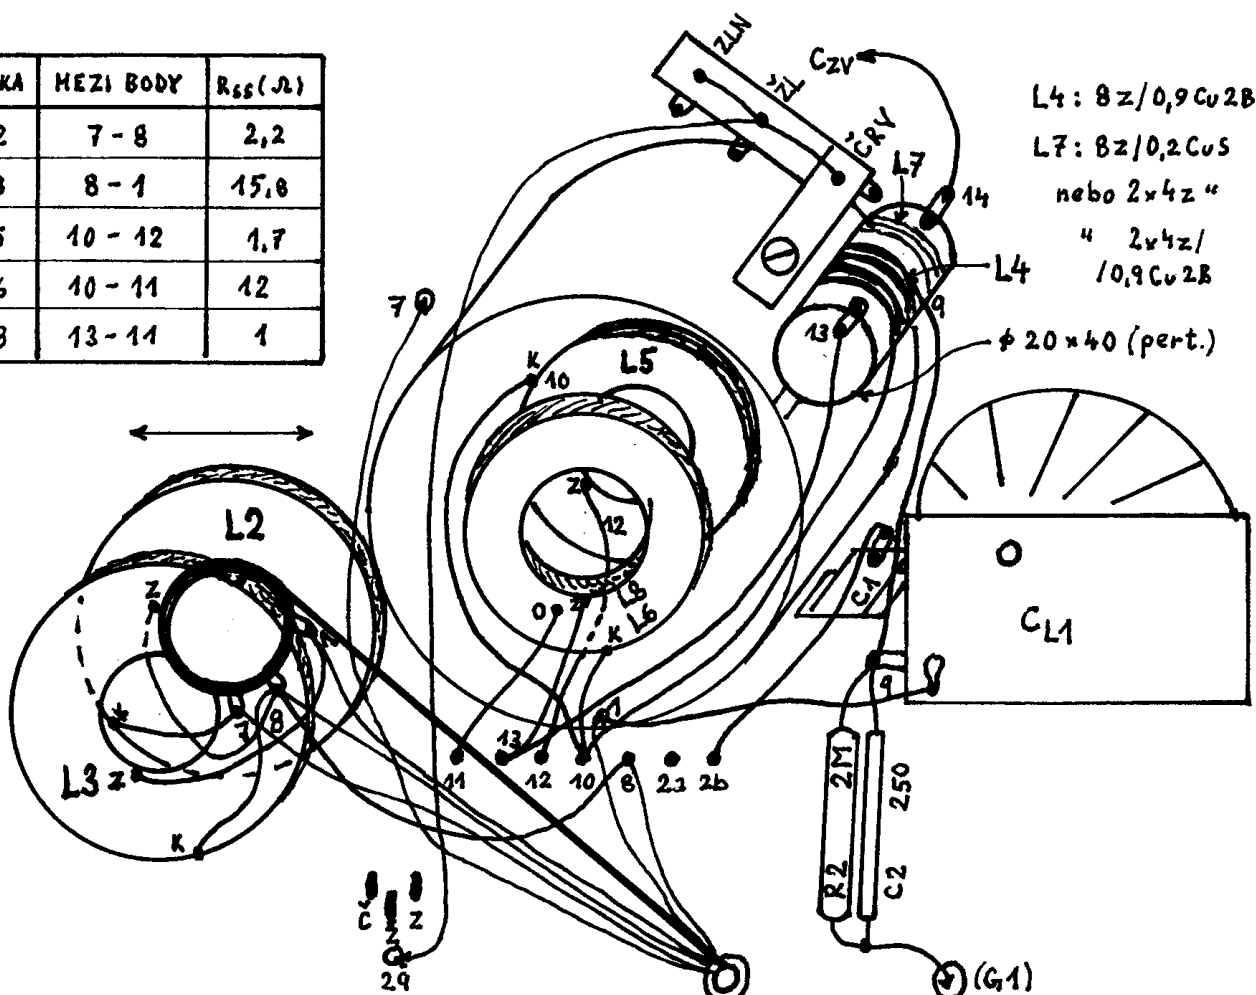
Rozložení součástí a vedení spojů pod šasi.
